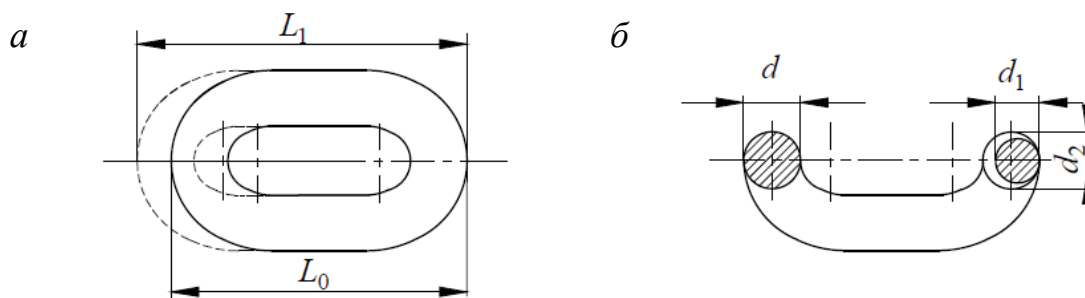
Браковка сварной цепи при: *a* – удлинении звена цепи; *б* – уменьшении диаметра сечения звена
